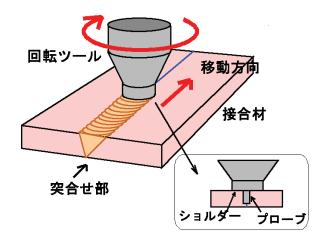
摩擦攪拌接合 (FSW) の原理 Principle of welding by FSW
